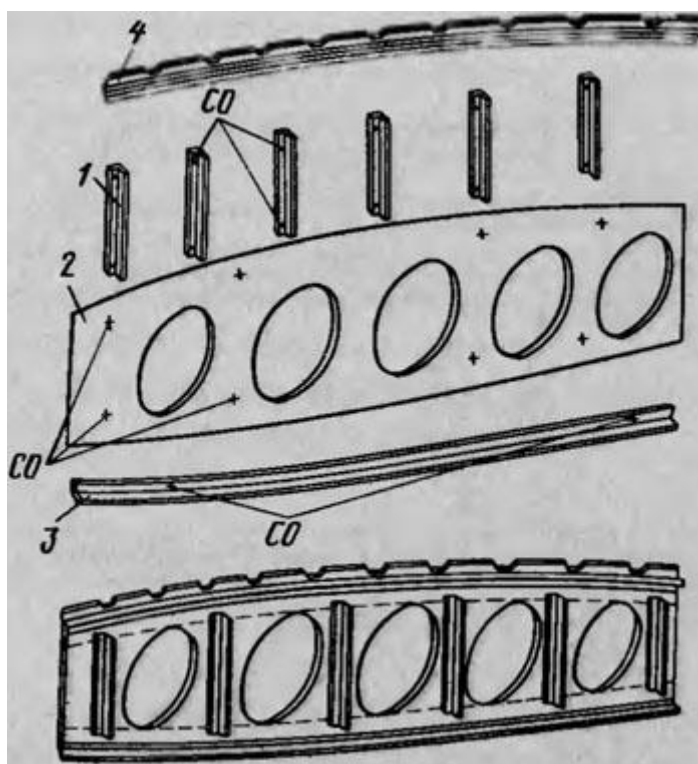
Схема сборки по сборочным отверстиям:
